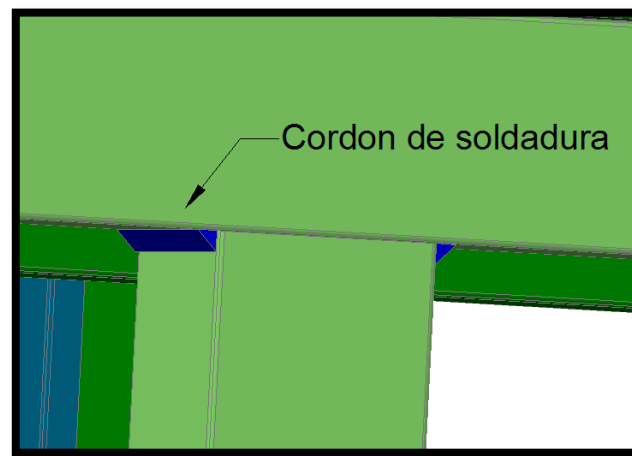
Localización de la soldadura en la mesa.
